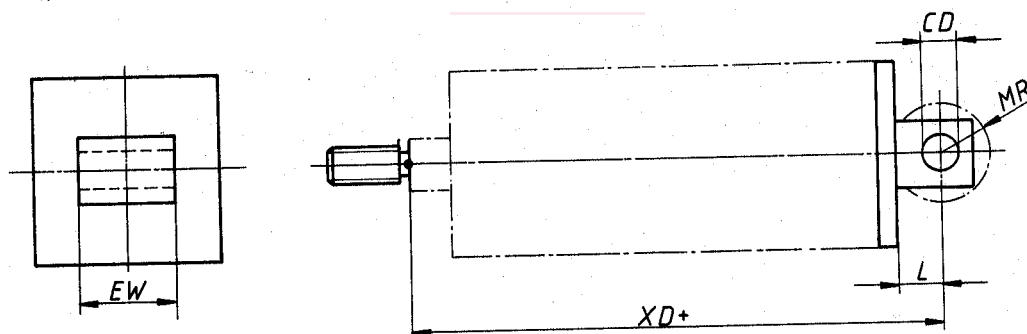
Fixation par tenon arrière démontable (MP 4)
